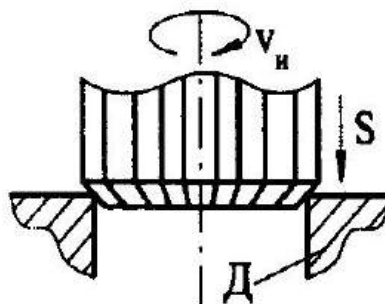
Схема оброблення деталей лезовим інструментом
